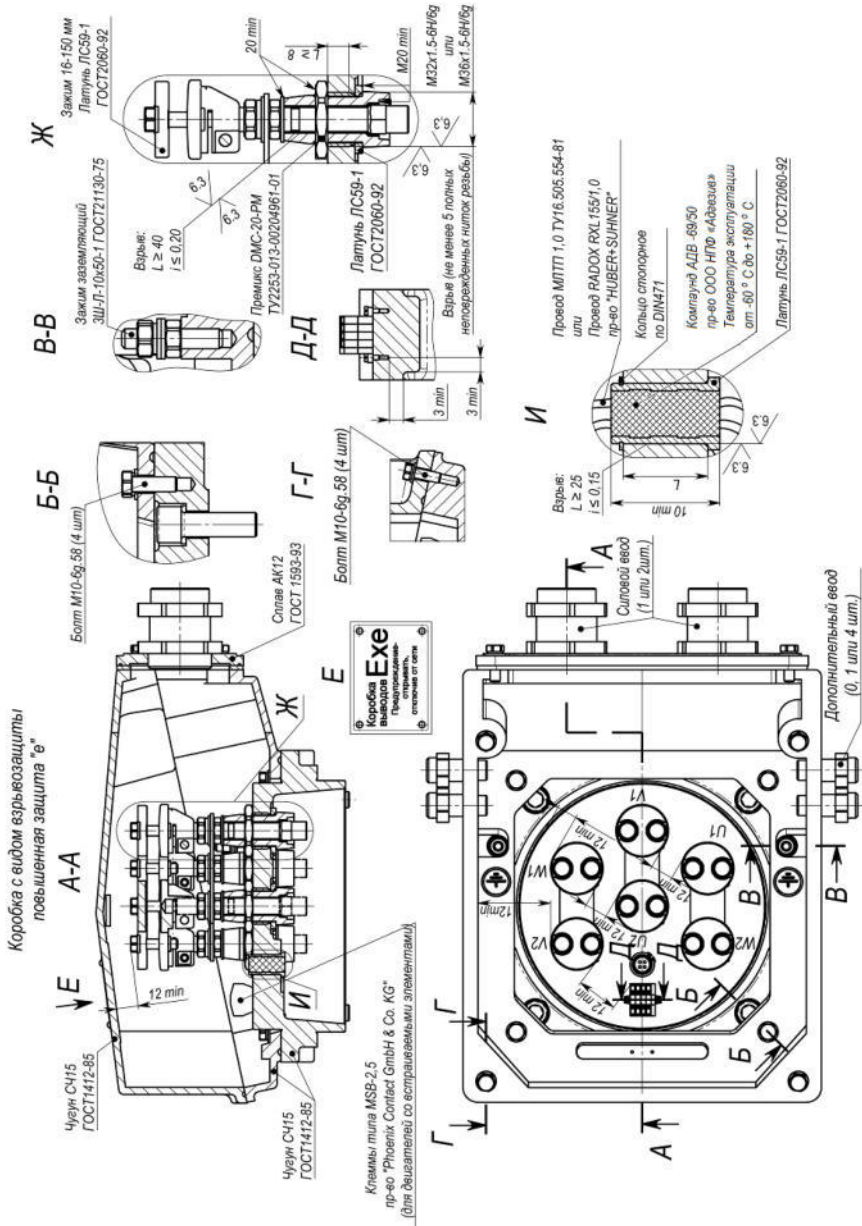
Чертеж взрывозащиты коробки выводов «е»
